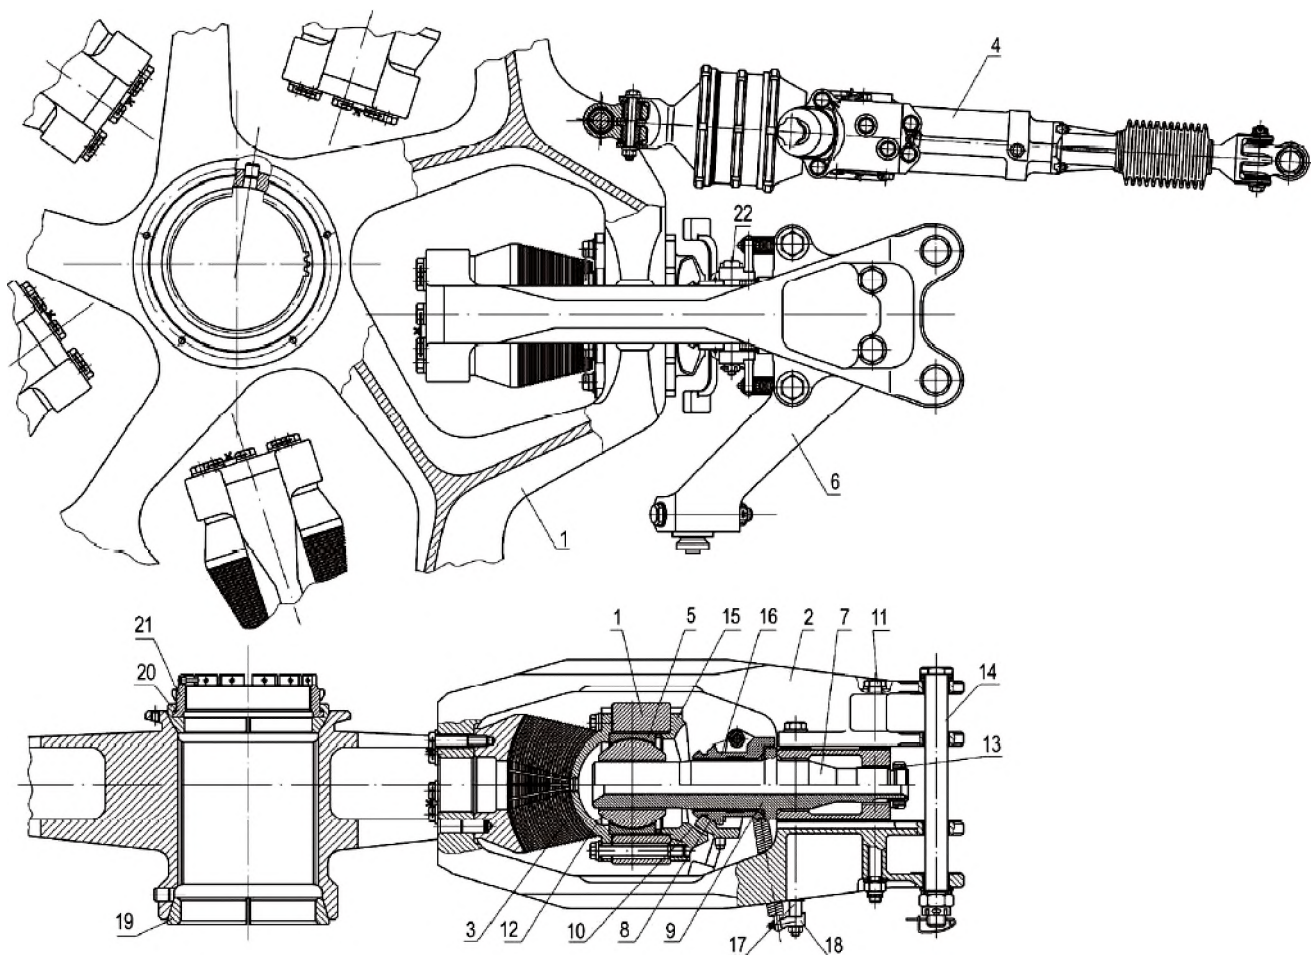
Конструкция втулки НВ с эластомерными подшипниками вертолета Ми-28 [11]:
